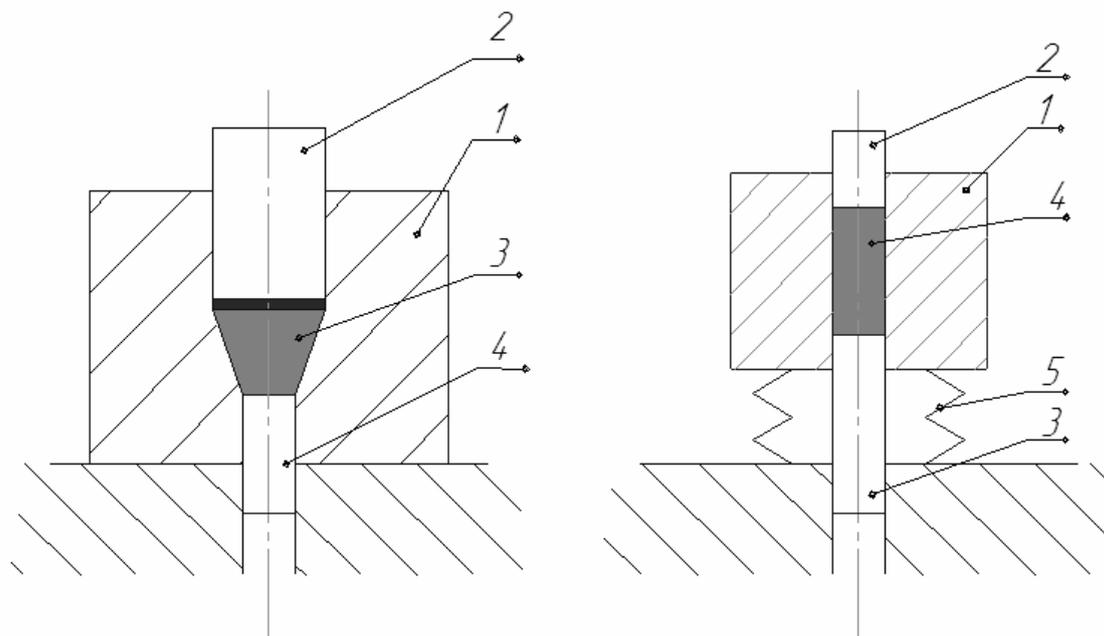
Схемы опробованных прессформ: а) с конической матрицей, б) с цилиндрической плавающей матрицей. 1-матрица, 2-пуансон, 3-выталкиватель, 4-брикет, 5-пружины.
